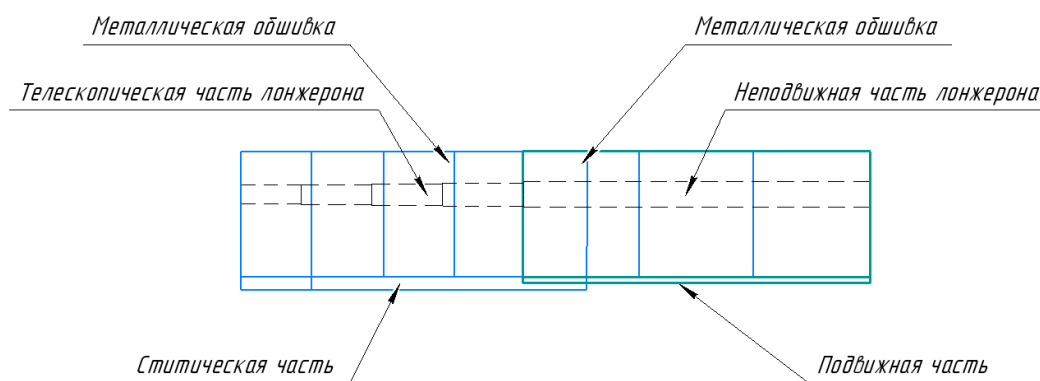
Схема конструкции консоли крыла с жесткой металлической обшивкой
